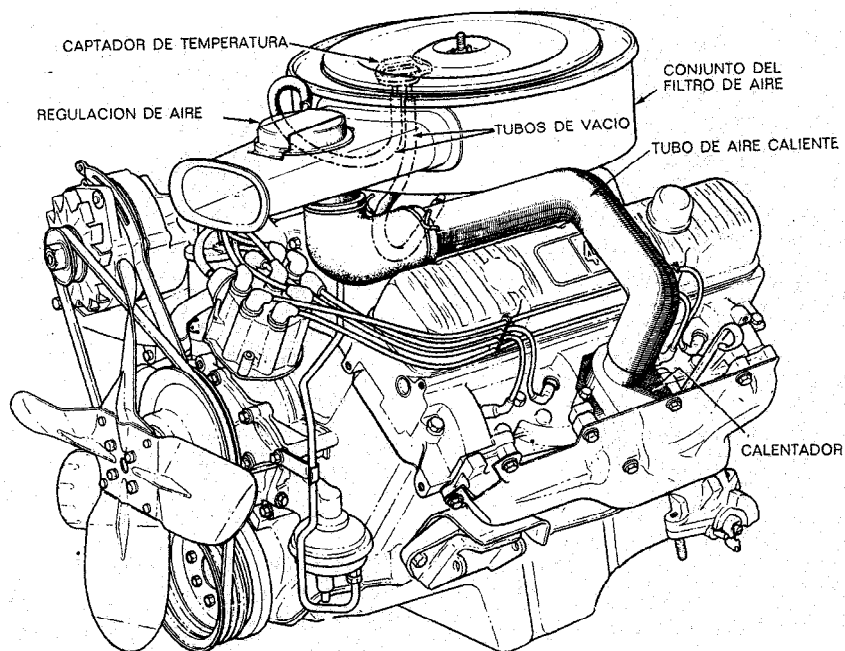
Sistema de aire precalentado sobre un motor de 8 cilindros en V (Buick Motor Division of General Motors Corporation).
